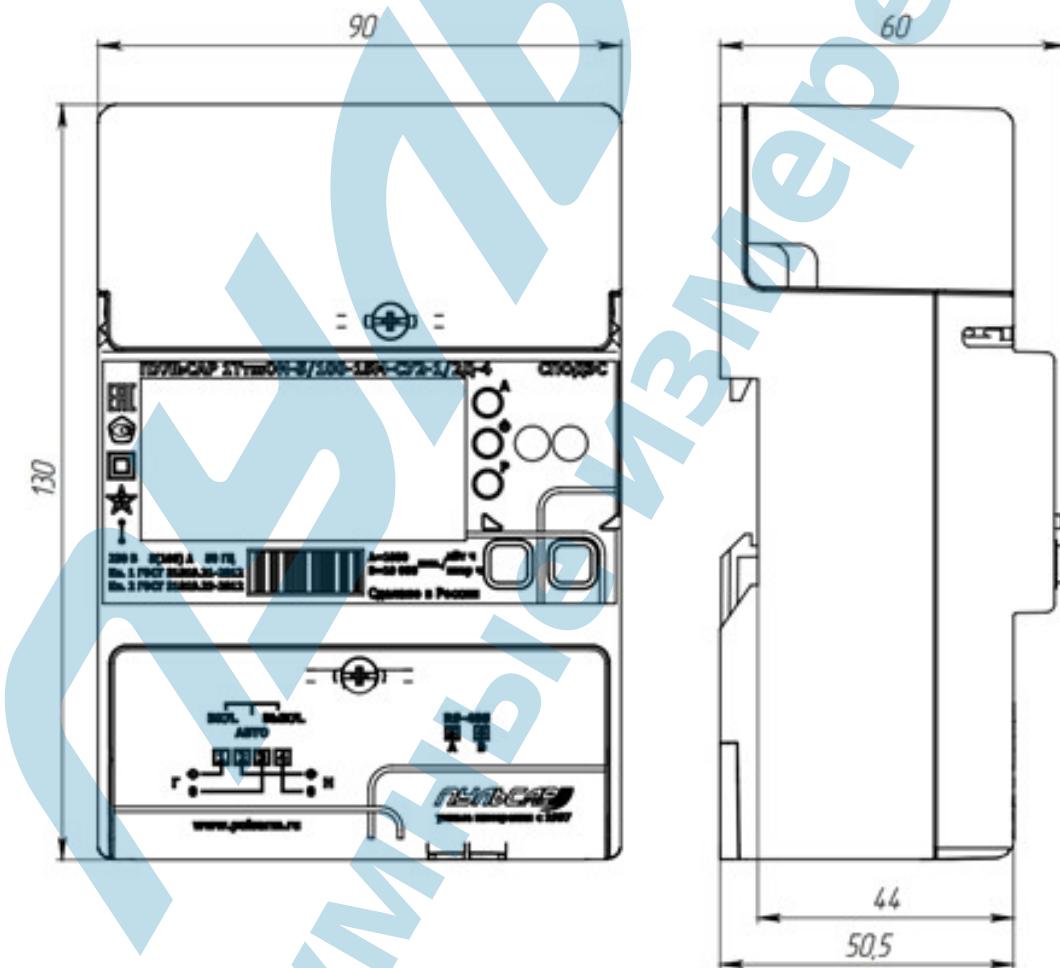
Габаритный чертёж компактного (малогабаритного) счётчика
